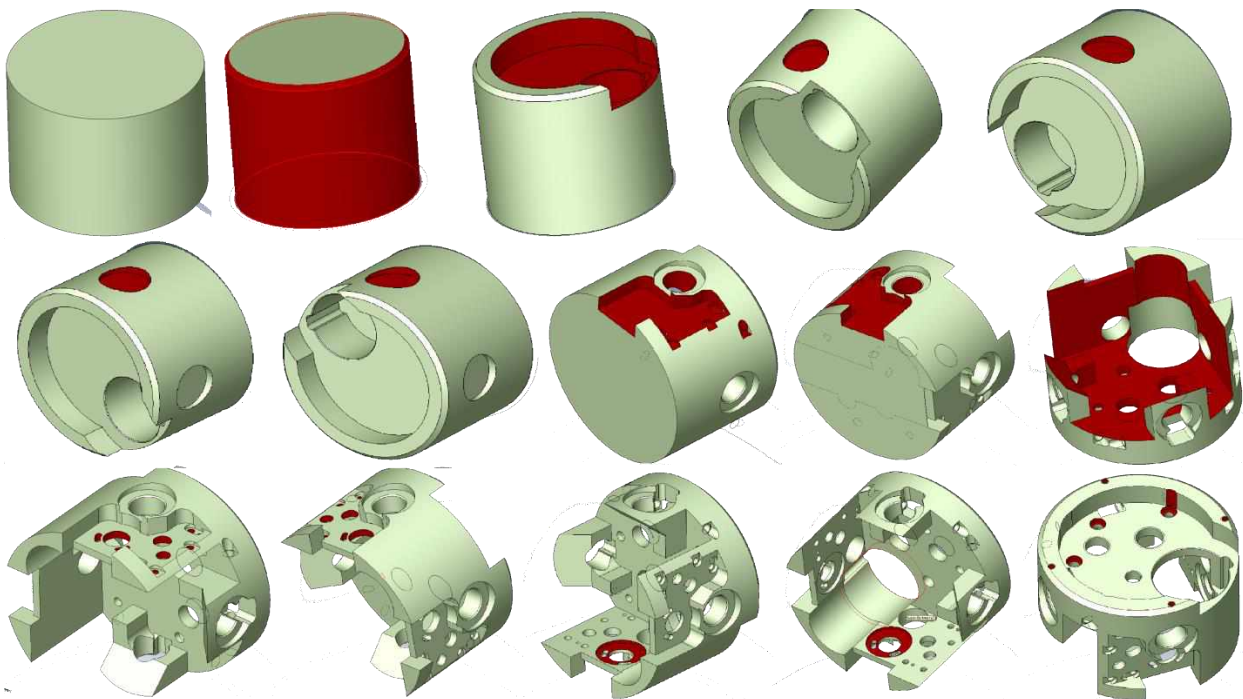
Комп'ютерна модель багатопераційної обробки деталі
